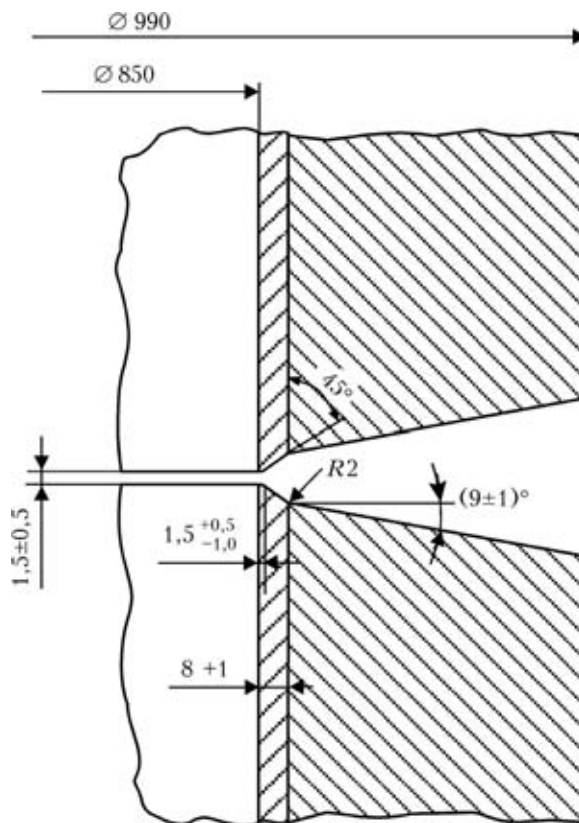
Схема разделки кромок для односторонней сварки трубного соединения из плакированной низколегированной стали
